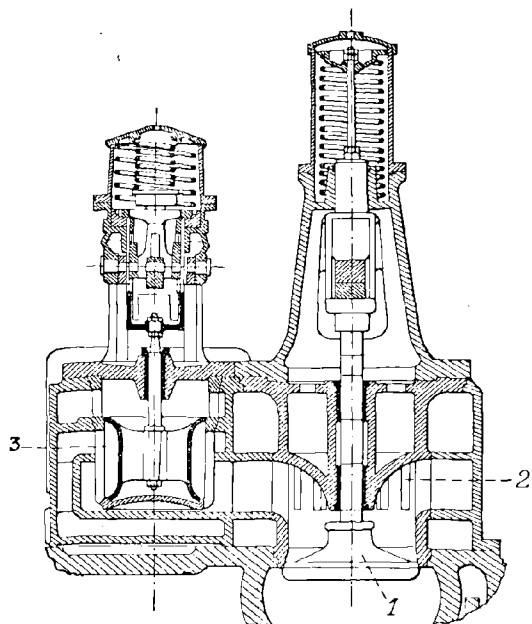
Soupape à double siège équilibrée et soupape d'admission du moteur de Nuremberg.
